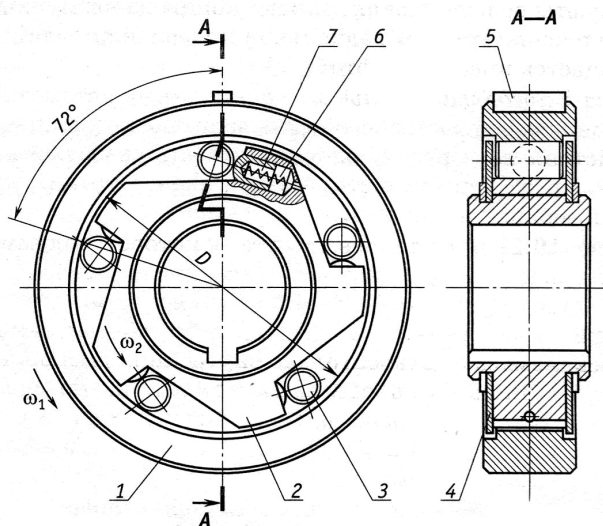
Обгонная муфта: 1 – обойма; 2 – звездочка; 3 – ролик; 4 – крышка; 5 – шпонка; 6 – пружина; 7 – поршень
